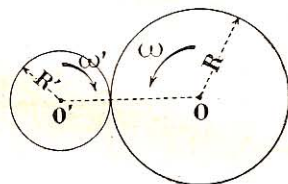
Velocidades de los engranajes y ruedas de fricción cilíndricas.
